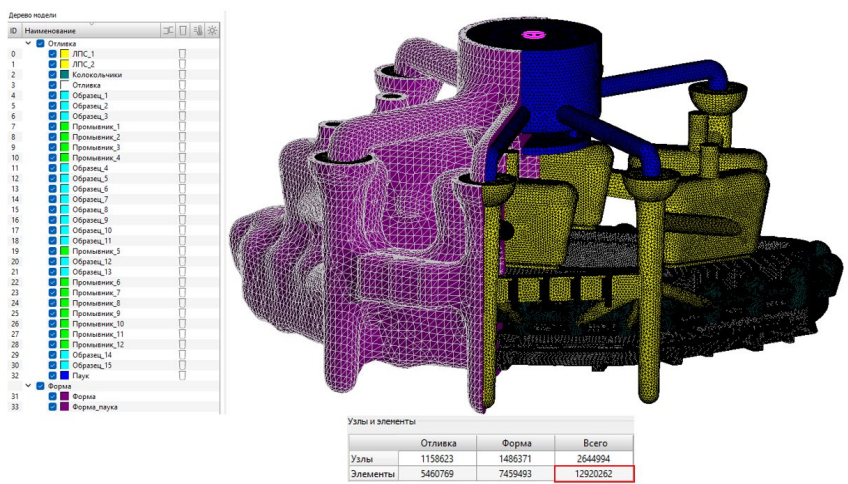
Отливка детали «Корпус с фланцами» с оптимизированной конструкцией ЛПС.
